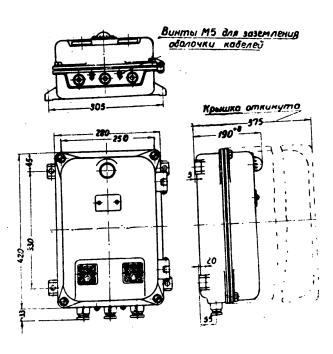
Габаритные размеры пускателя переменного тока типа OПТ-160У
